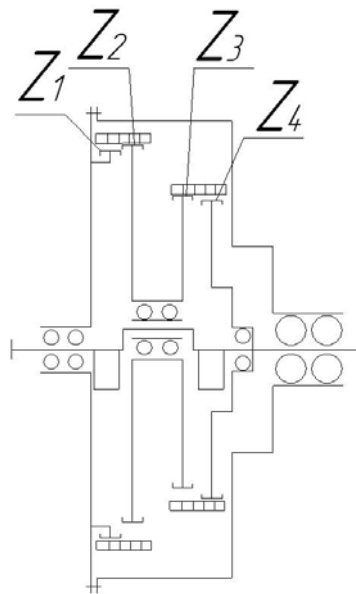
Схема планетарного редуктора с четырьмя звездочками
